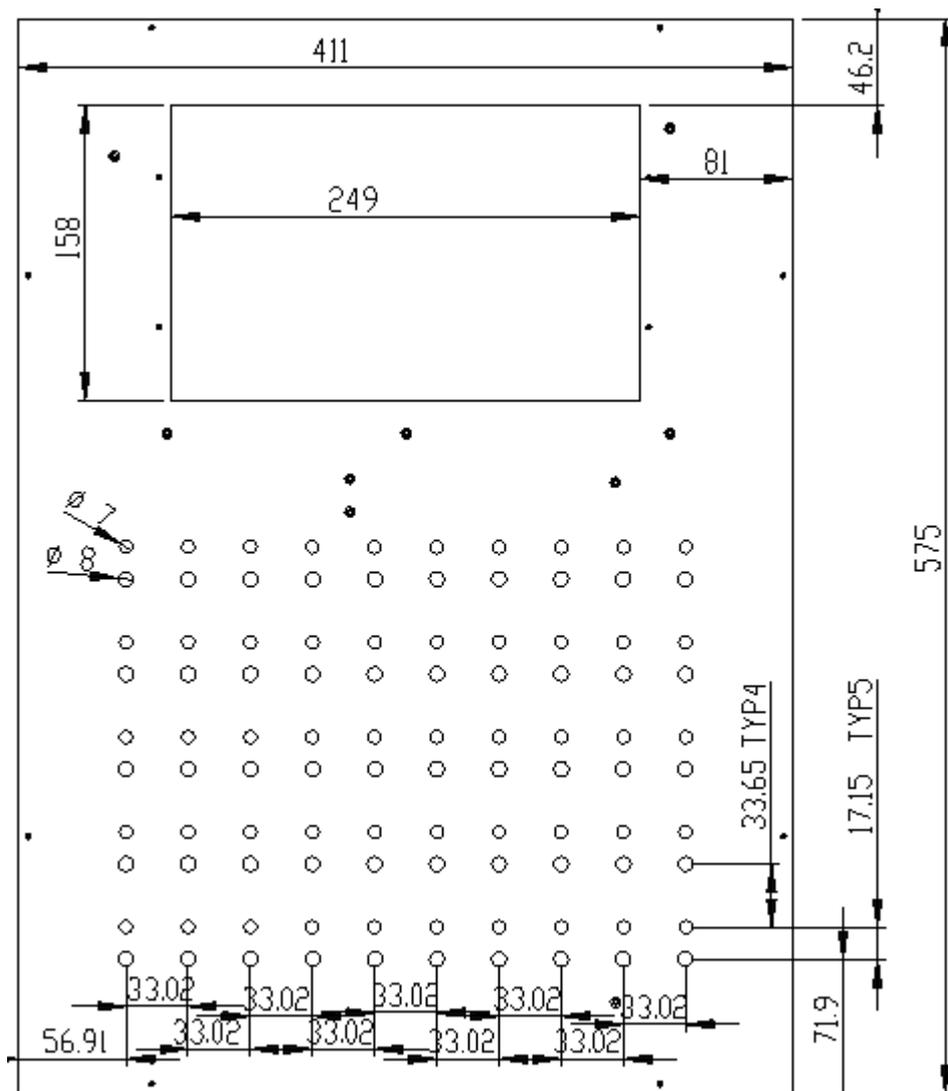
Dimensioni del Pannello Anteriore di Platinum Touch 50
